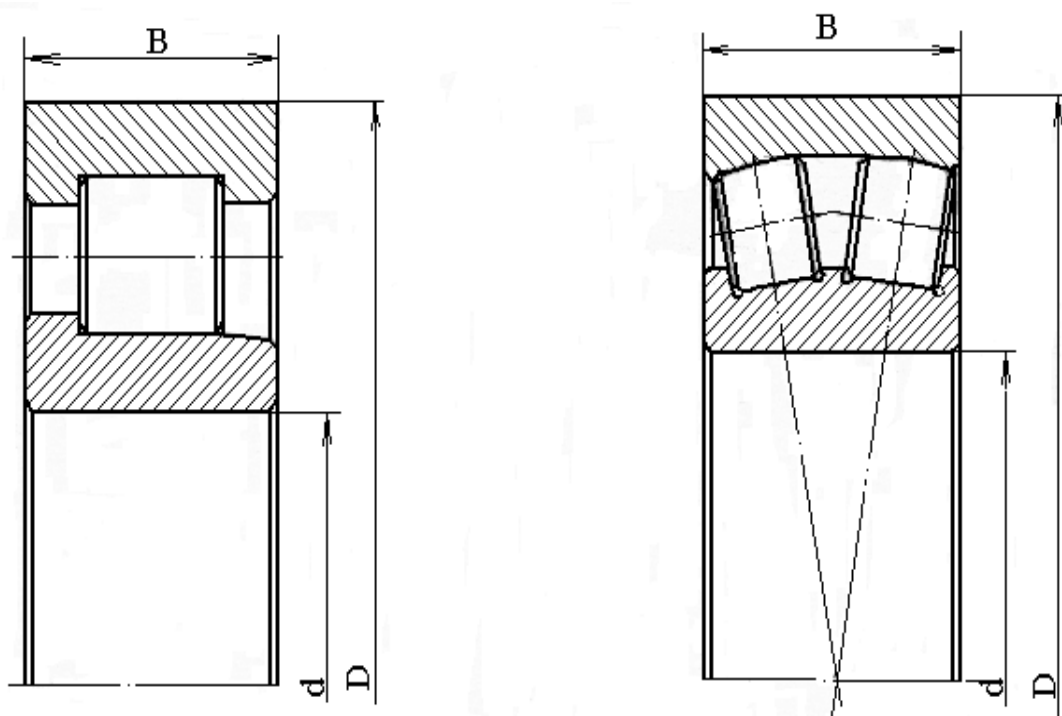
В.3 – Подшипник роликовый, радиальный, с короткими цилиндрическими роликами
